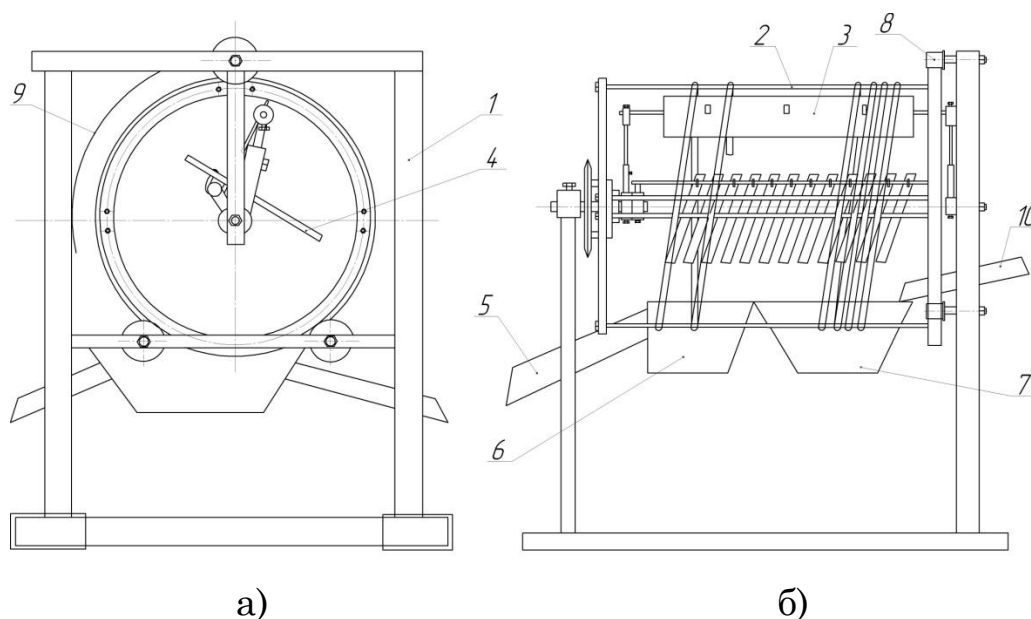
Быстроходное роторно-винтовое устройство для разделения клубнеплодов:
